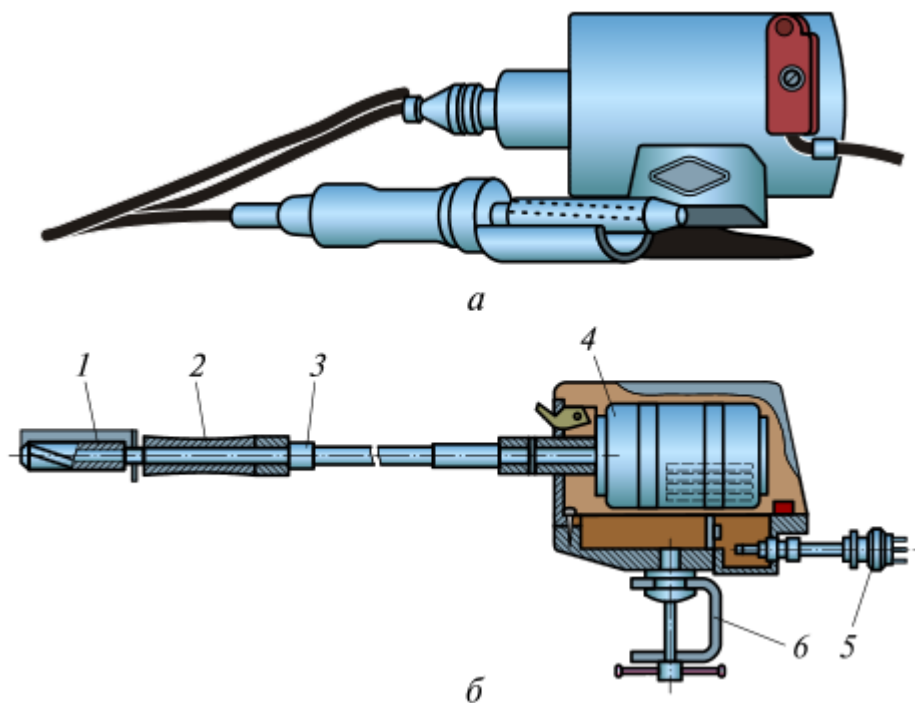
Рыбоочистительная машина РО-1М: *а* — общий вид; *б* — разрез: 1 — скребок; 2 — рукоятка; 3 — гибкий вал; 4 — электродвигатель; 5 — вилка; 6 — кронштейн
